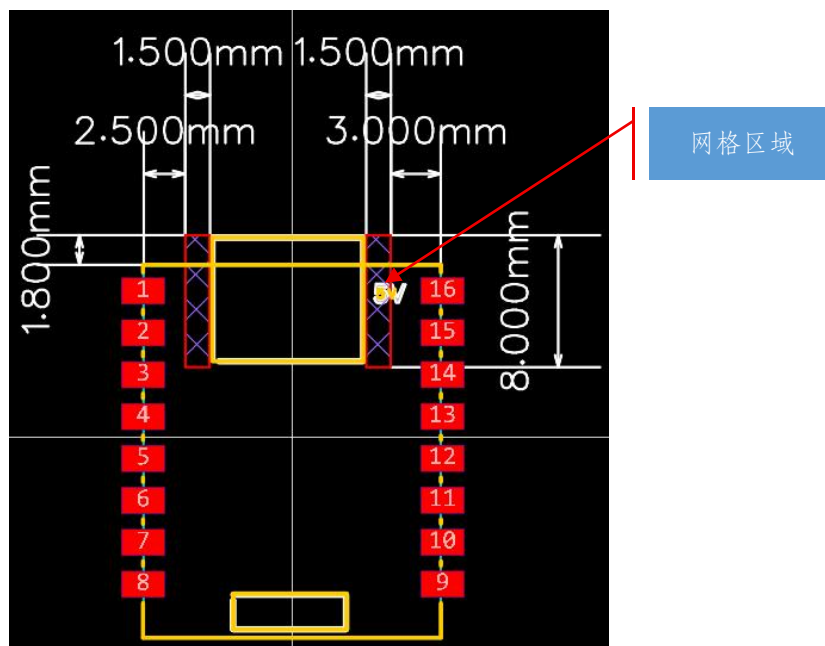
ESP32-C3 单片机模块在 PCB 板上禁止布线区域说明
